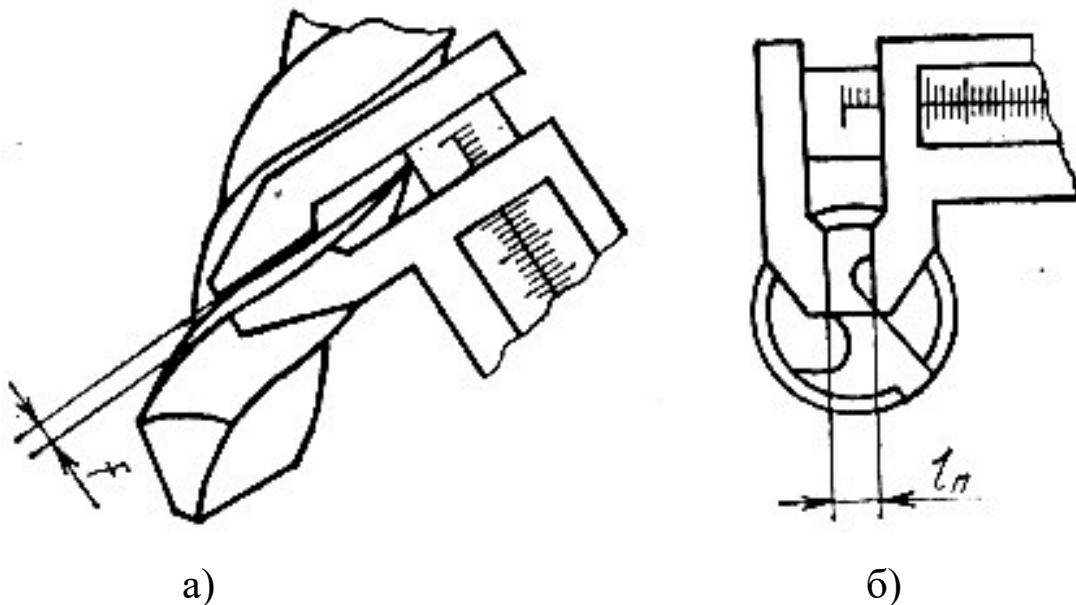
Вимірювання ширини направляючої стрічки  $f$  (а) та довжини поперечної кромки свердла  $l_n$  (б)
